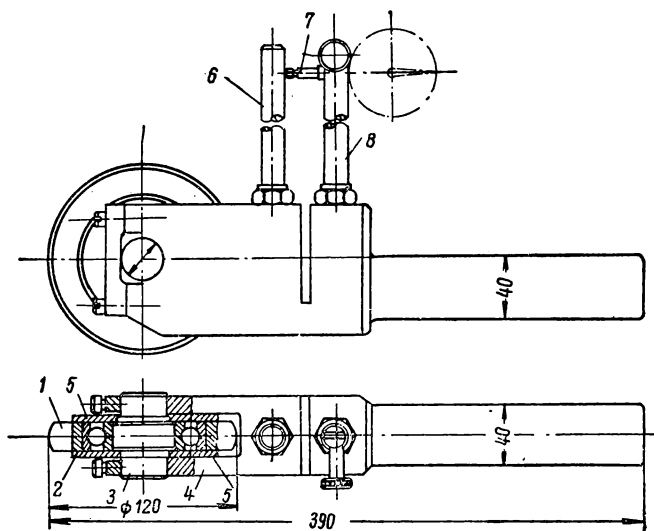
Державка с роликом для обкатывания гладких цилиндрических поверхностей.
